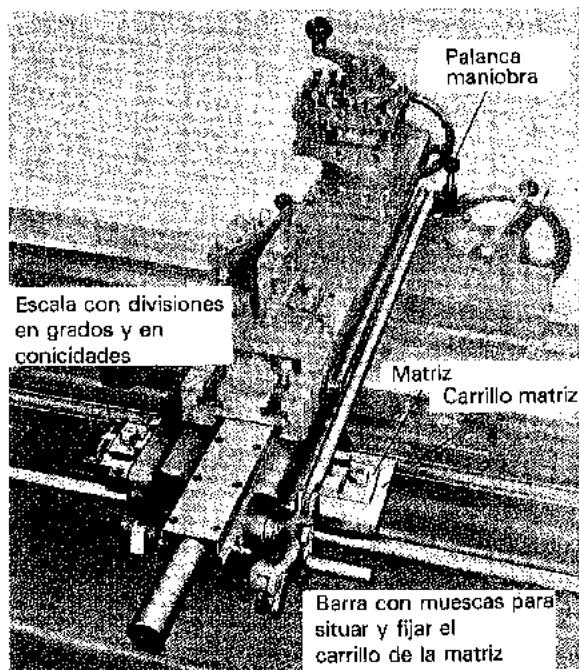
Aparato para conos (Jones & Lamson Machine Co.)
